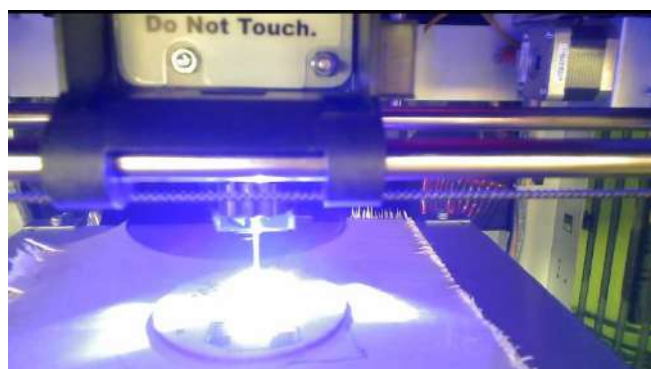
Процесс нанесения логотипа на заготовку брелка
